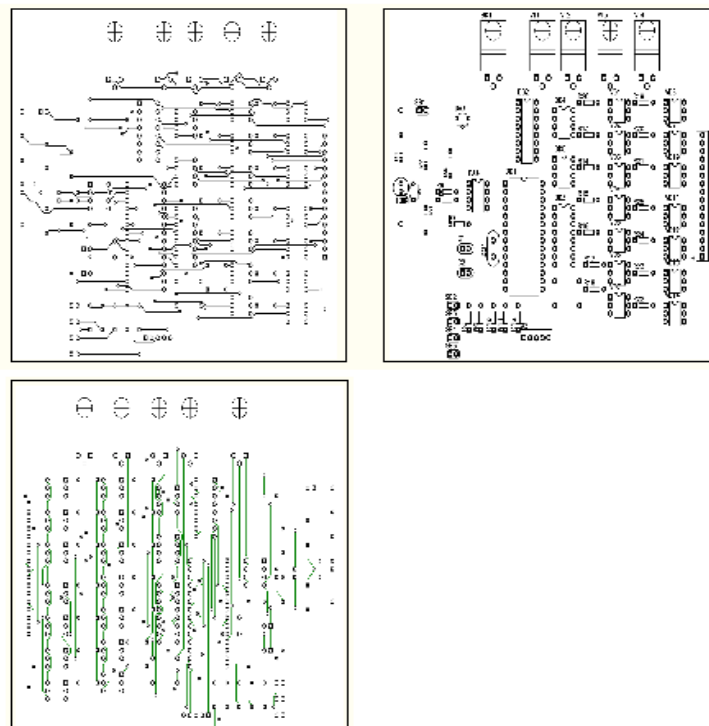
Верхний, нижний слои платы и сборочный чертеж
